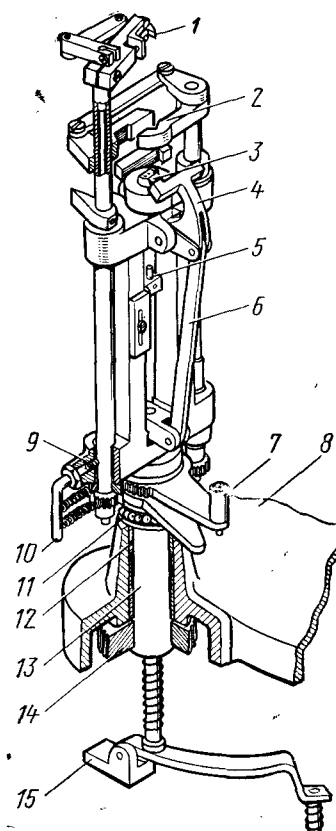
Станок для заштамповки гребешковых ножек.
